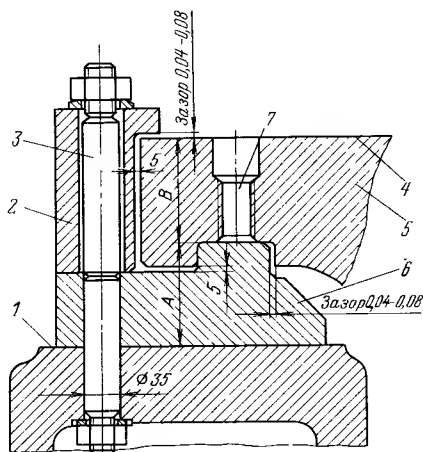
Опираие корпуса турбины на подшипник с помощью лап:
